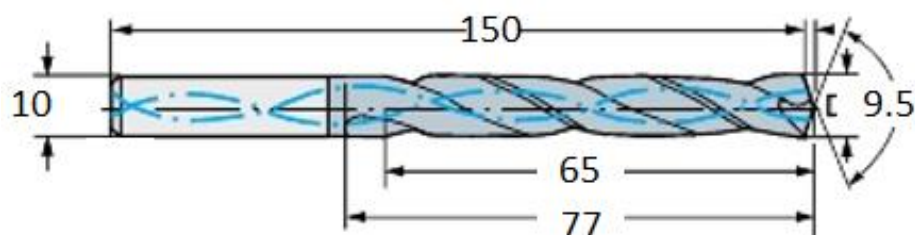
сверло Sandvik Coromant CoroDrill 460.1-0950-071A1-XM GC34
